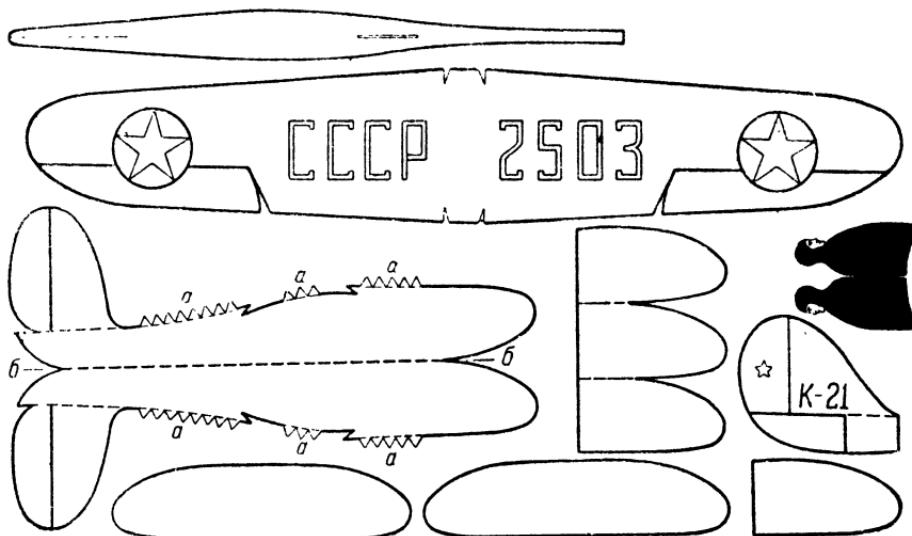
Рабочие чертежки частей, из которых изготавливается модель.
